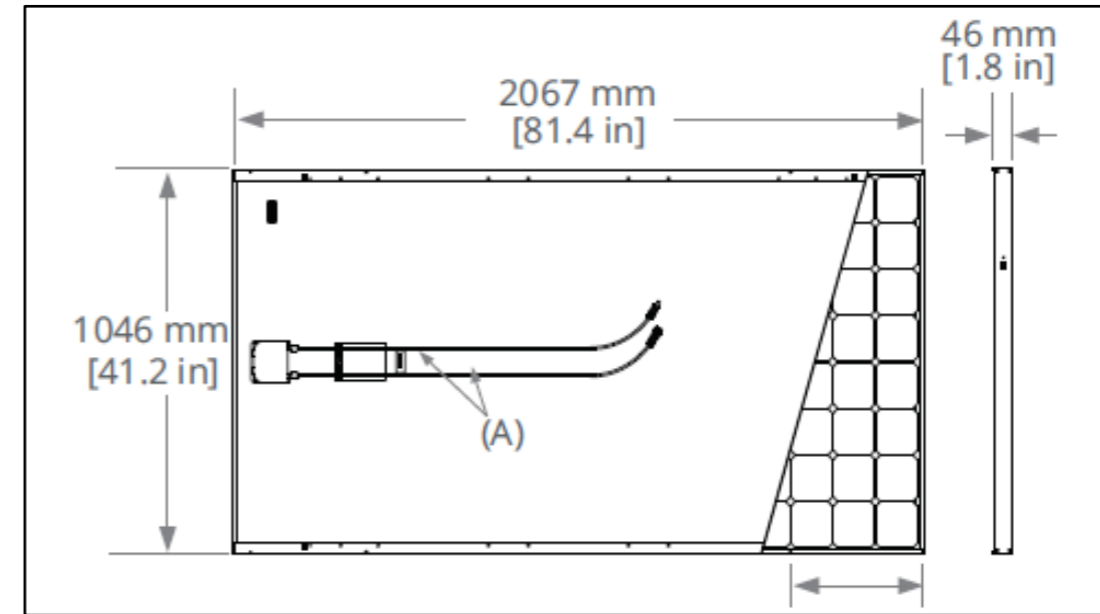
Schéma d'un panneau (source : Sun Power 440 Wc)
